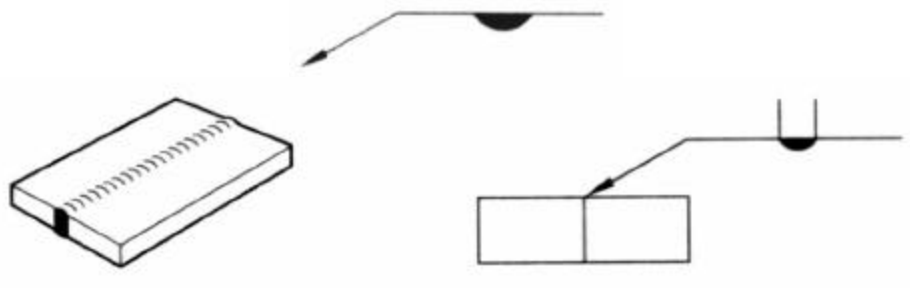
Solda de um Lado com Projeção no Lado Oposto
